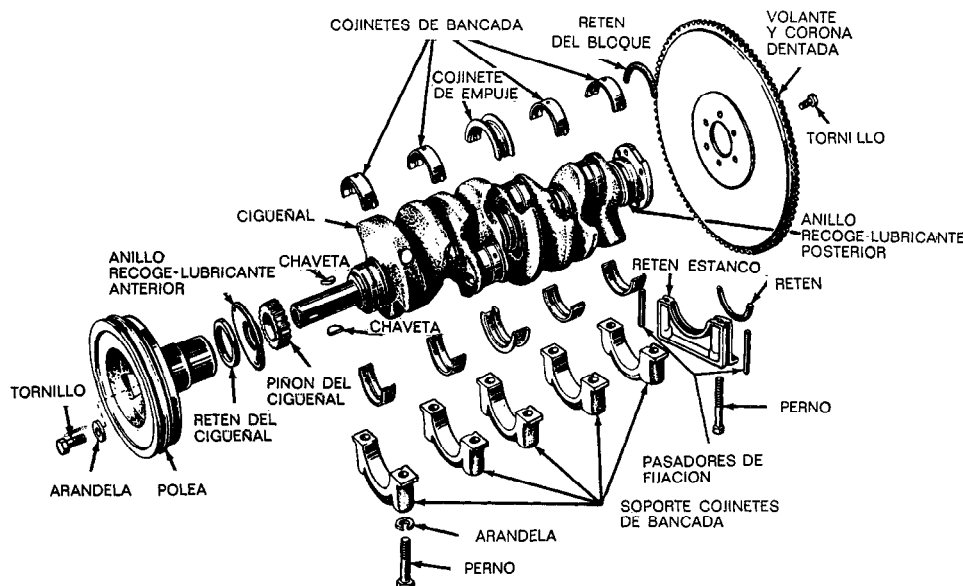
Cigüeñal y partes anexas de un motor de 8 cilindros en V (*Lincoln-Mercury Division of Ford Motor Company*).
